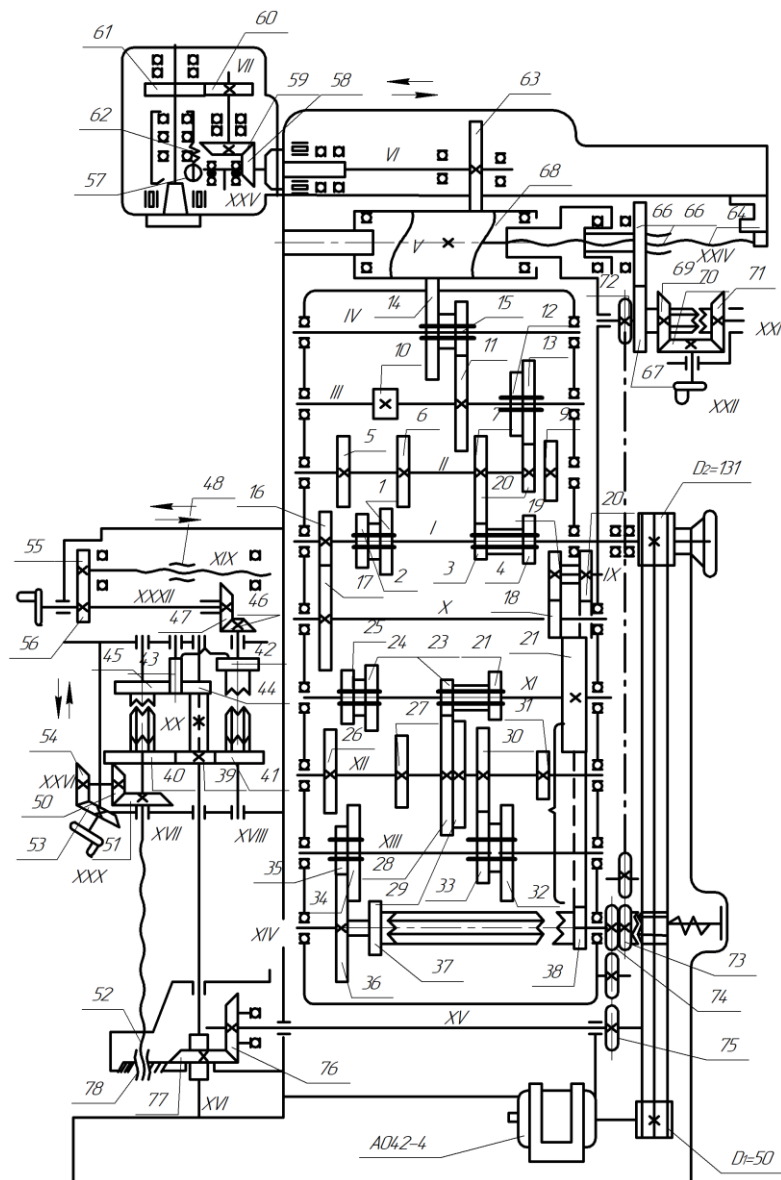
Кінематична схема фрезерного інструментального широкоуніверсального верстата 676П
